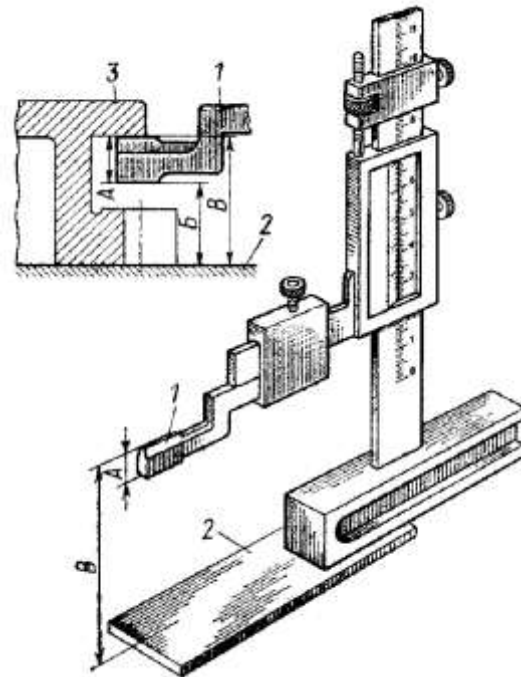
Штангенрейсмус: 1 – губка; 2 – розмічувальна плита; 3 – виливок; А – висота губки; Б – показання за шкалою штангенрейсмуса; В – контрольований розмір виливка
